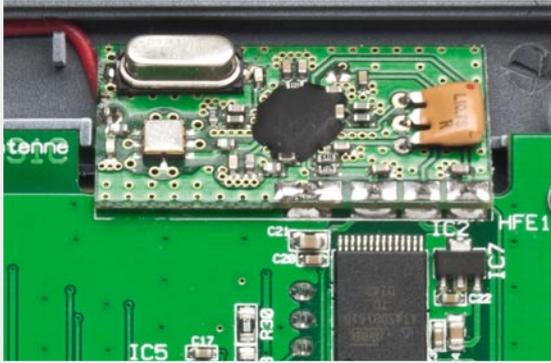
Das Empfangsmodul HFE 1 wird schräg im Gehäuse liegend aufgelötet, weshalb zuvor die Hauptplatine in die Gehäusefront zu schrauben ist.
